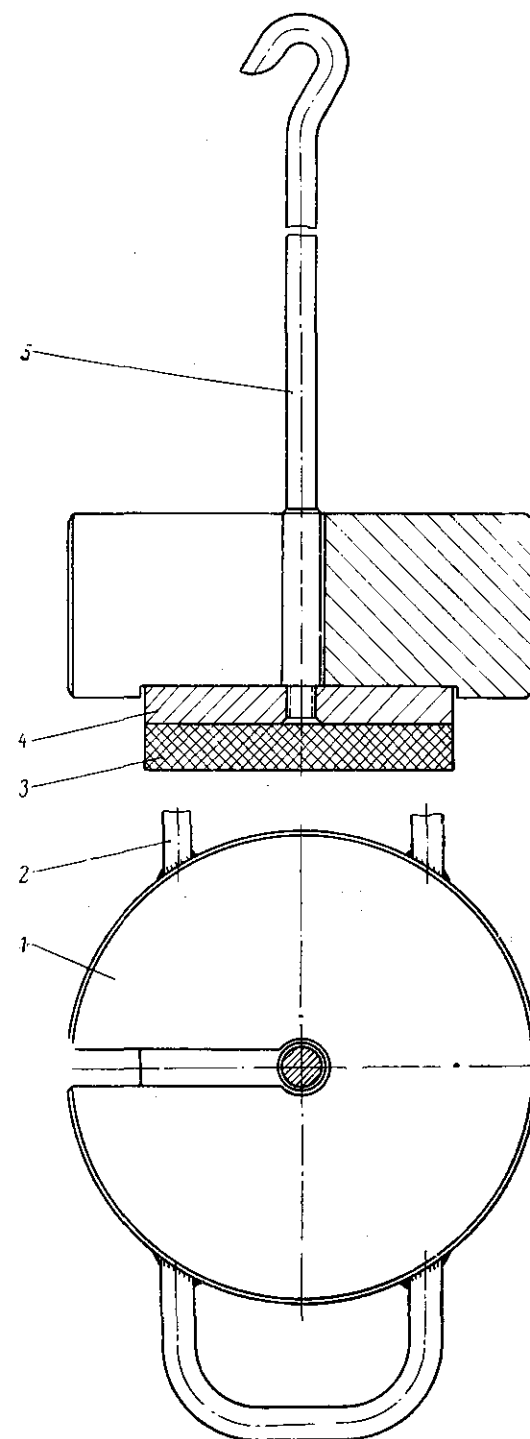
Приспособление 63509/738 для проверки люфта стакана:
